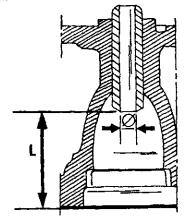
Размер "L" определяет высоту установки направляющих втулок клапанов на двигателях типа XU.
